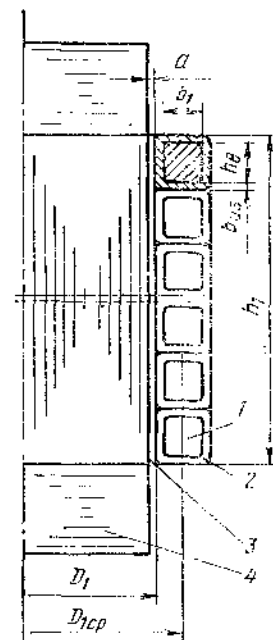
Эскиз индуктора: 1 — индуктор; 2 — изоляция индуктора; 3 — изолирующий цилиндр; 4 — сердечник
